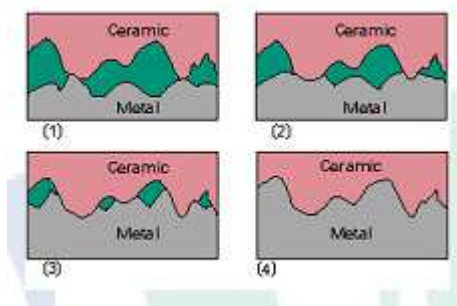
Sequencia de soldagem por difusão. Fonte: www.ewf.eb
